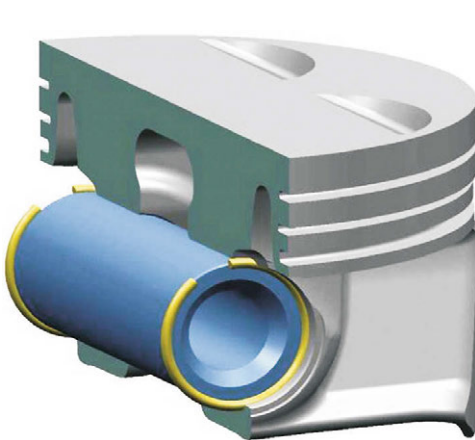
Pkw-Kolben mit Runddrahtspreng-ring Form C nach DIN 73130
